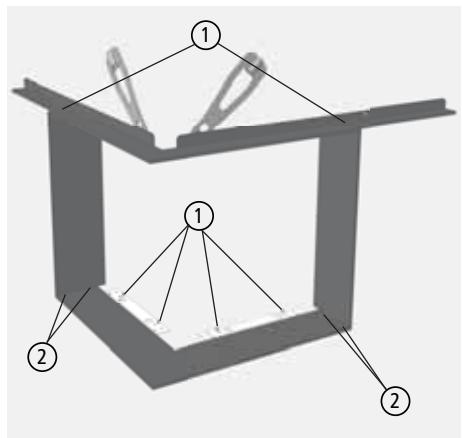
notwendige Schrauben für Anbaurahmen
